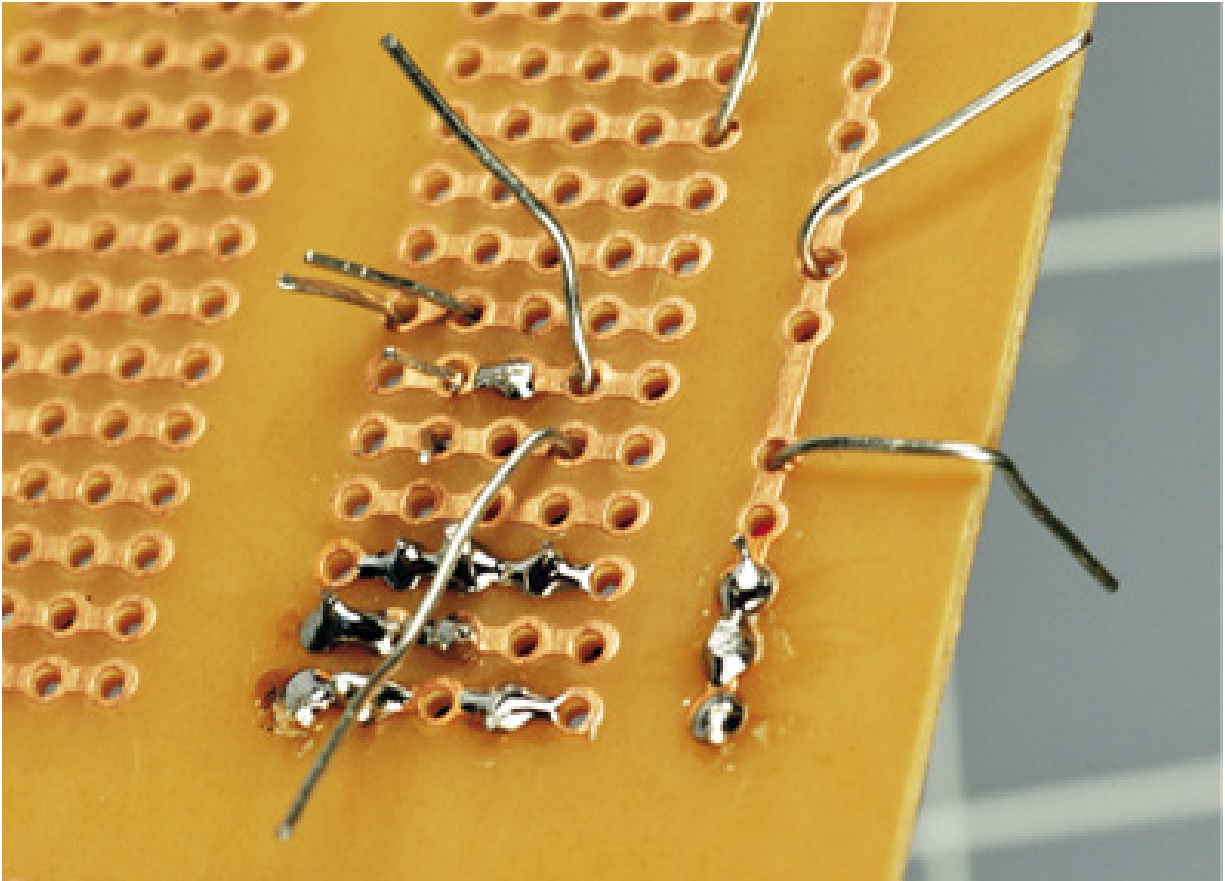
Depois que a solda esfriar e endurecer, corte o fio saliente.
